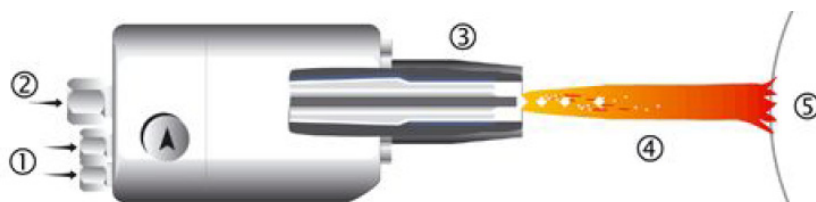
Схема сверхзвукового газопламенного напыления
